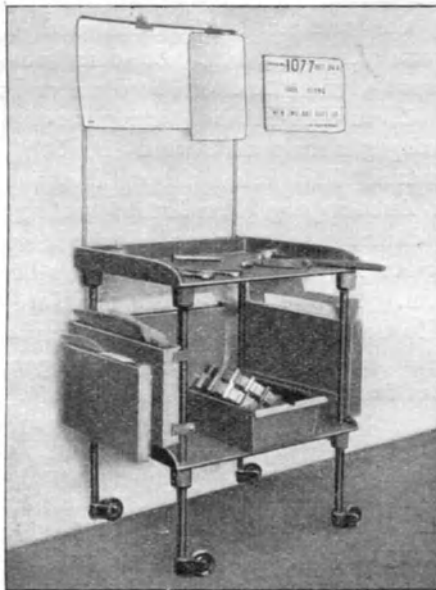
Ausrüstung eines Werkzeugkarrens, der mit allen, zu einer bestimmten Arbeit benötigten Werkzeugen ausgerüstet ist.
